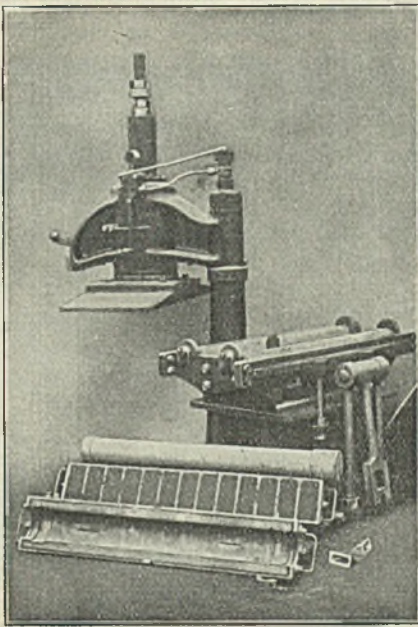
Universalmaschine für Fallrohre mit fertiggepreßten Kästen.
